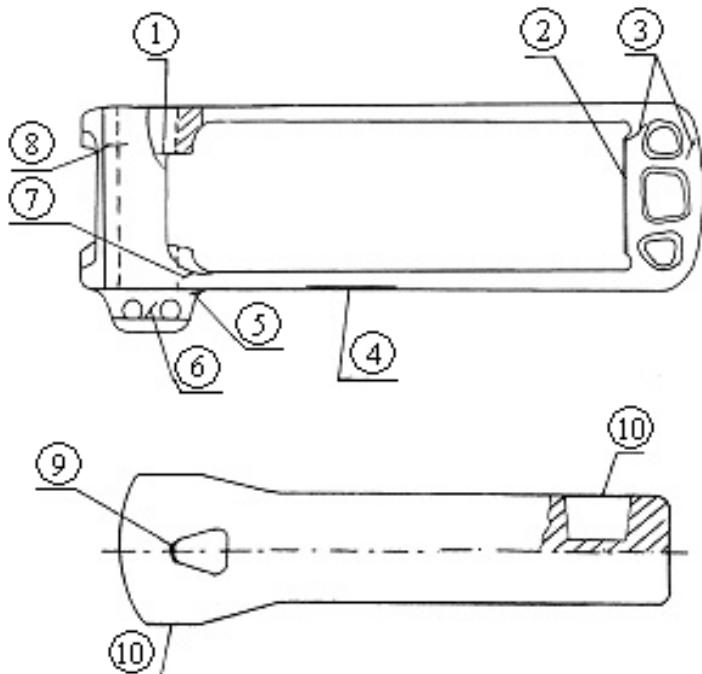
Дефекты хомута тягового, ремонтируемые сваркой или наплавкой
